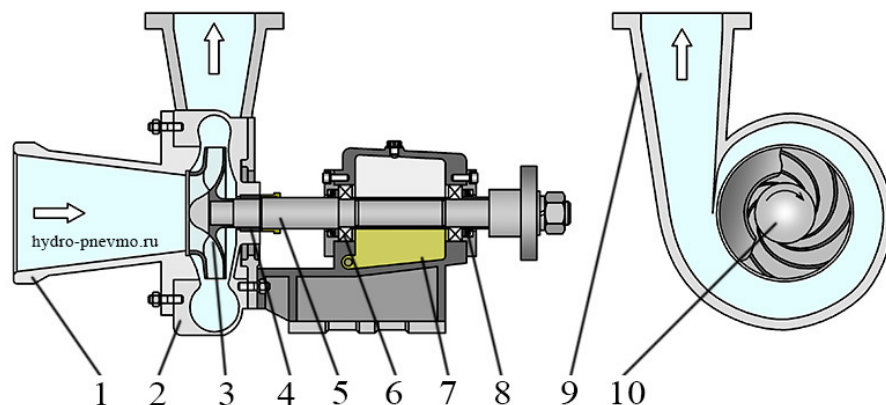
Схема відцентрового насоса: 1-вхідний патрубок; 2- спіральний відвід; 3- робоче; 4-ущільнення робочої камери; 5-вал; 6- підшипник; 7-порожнина змащування підшипників; 8- манжета; 9- дифузор; 10- гайка- обтікач
